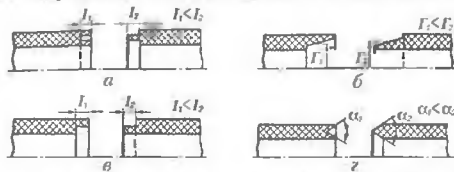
Конструкції розробки кромки труб під зварювання тертям:
